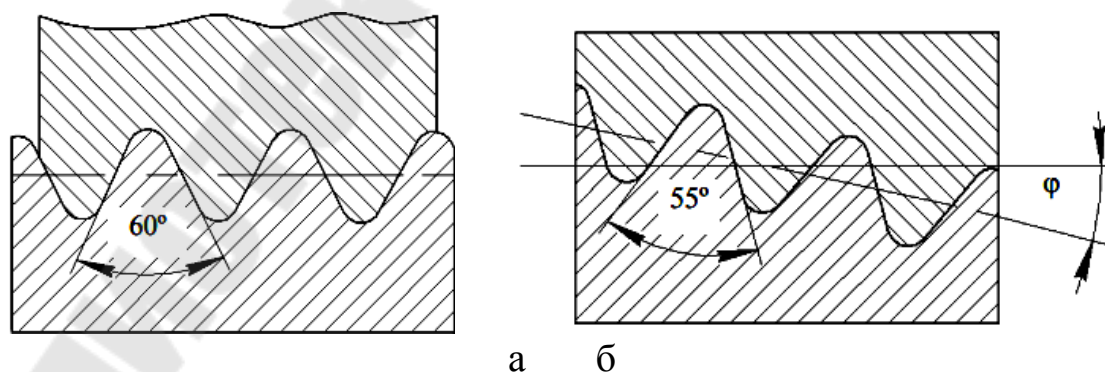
Крепежно-уплотняющие резьбы: а – цилиндрическая; б – коническая
